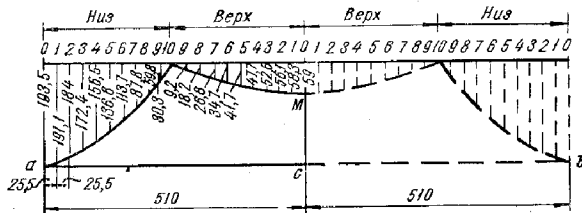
Развертка конца трубы II разветвленного сварного тройника (штапов).
